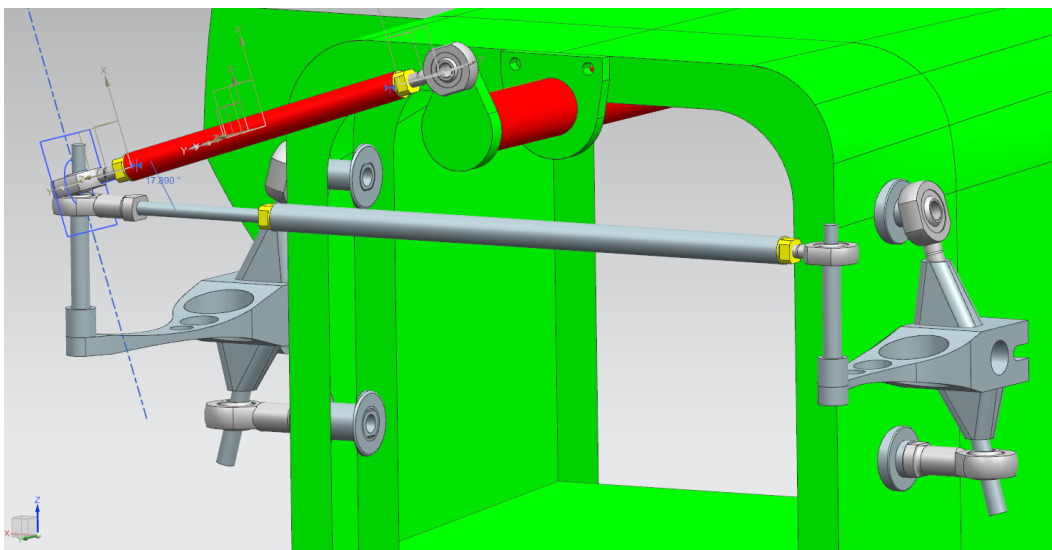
Colocación en el sistema de la leva la columna de dirección y la varilla empujadora.
